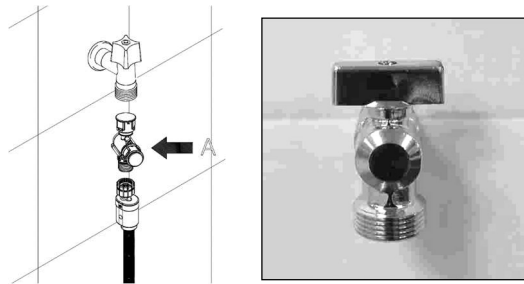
Beim Anschließen des Zulaufschlauchs die mitgelieferten Siebe einsetzen.
